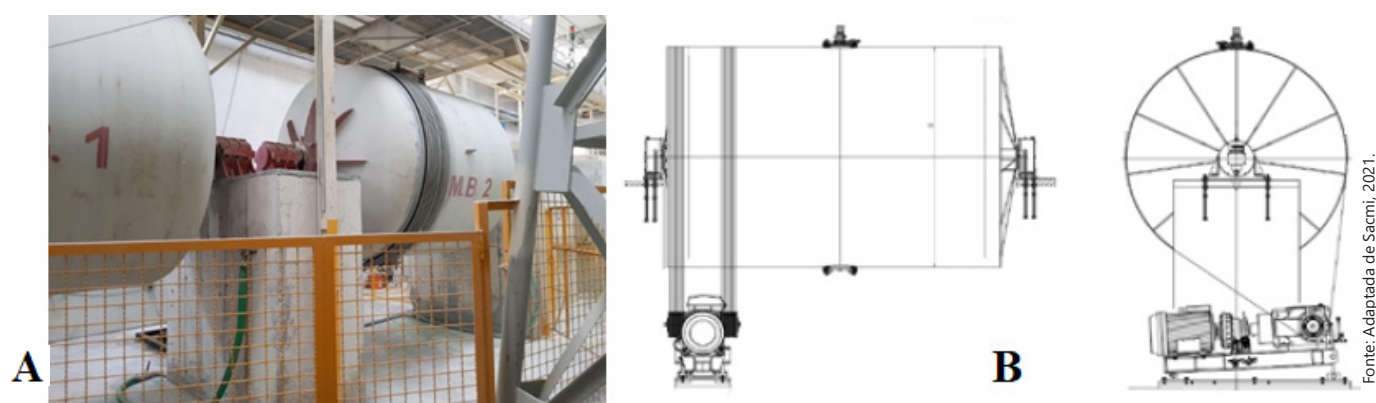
A) Moinho de bolas descontínuo. B) Vista lateral e frontal.
